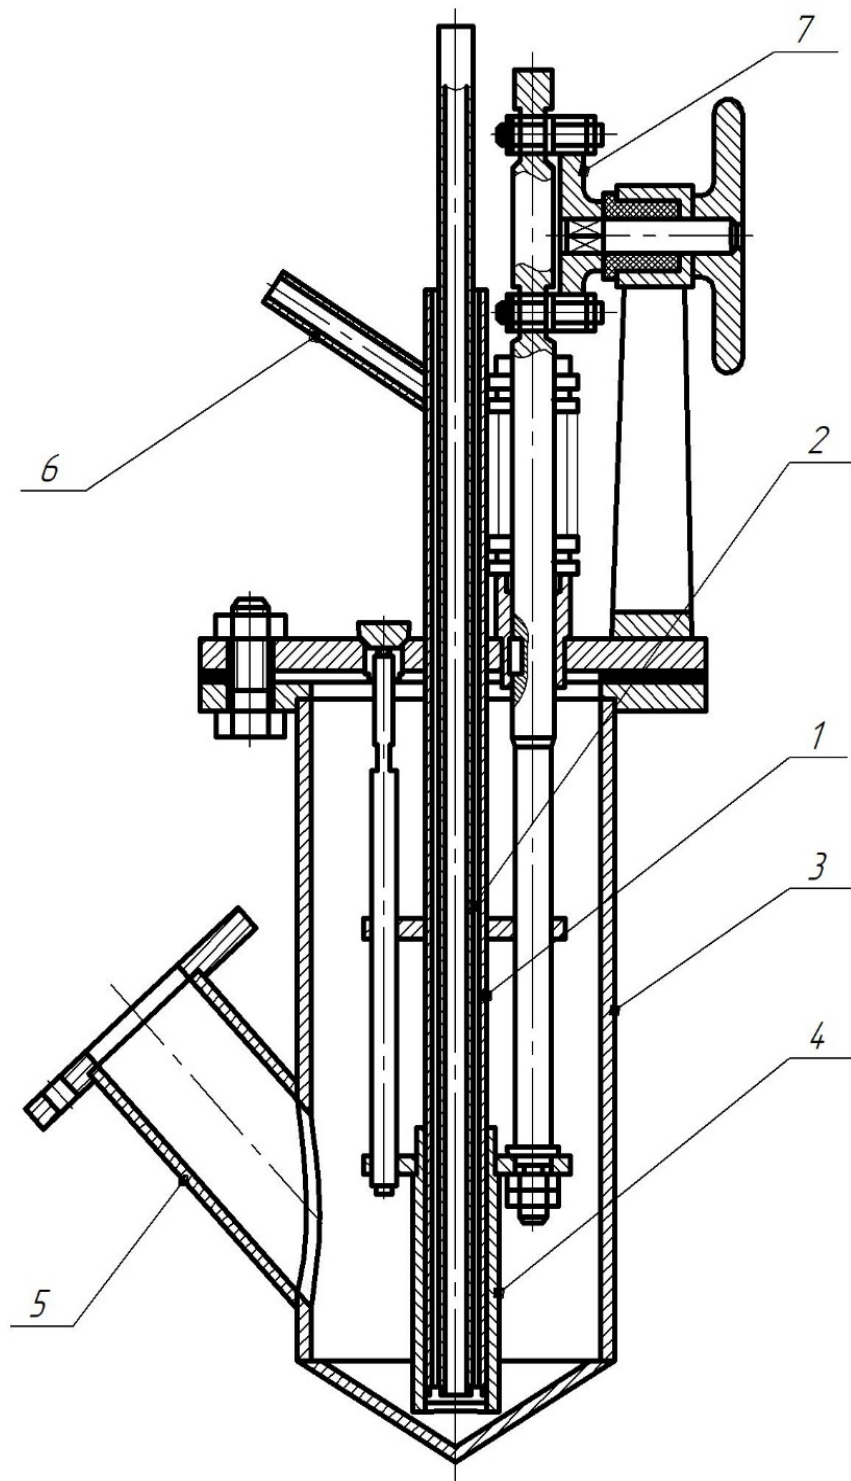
Ерліфтна установка з шиберам: 1 – повітропровід; 2 – напірна труба; 3 – резервуар; 4 – циліндр; 5 та 6 – штуцер; 7 – механізм підйому та опускання шибера
